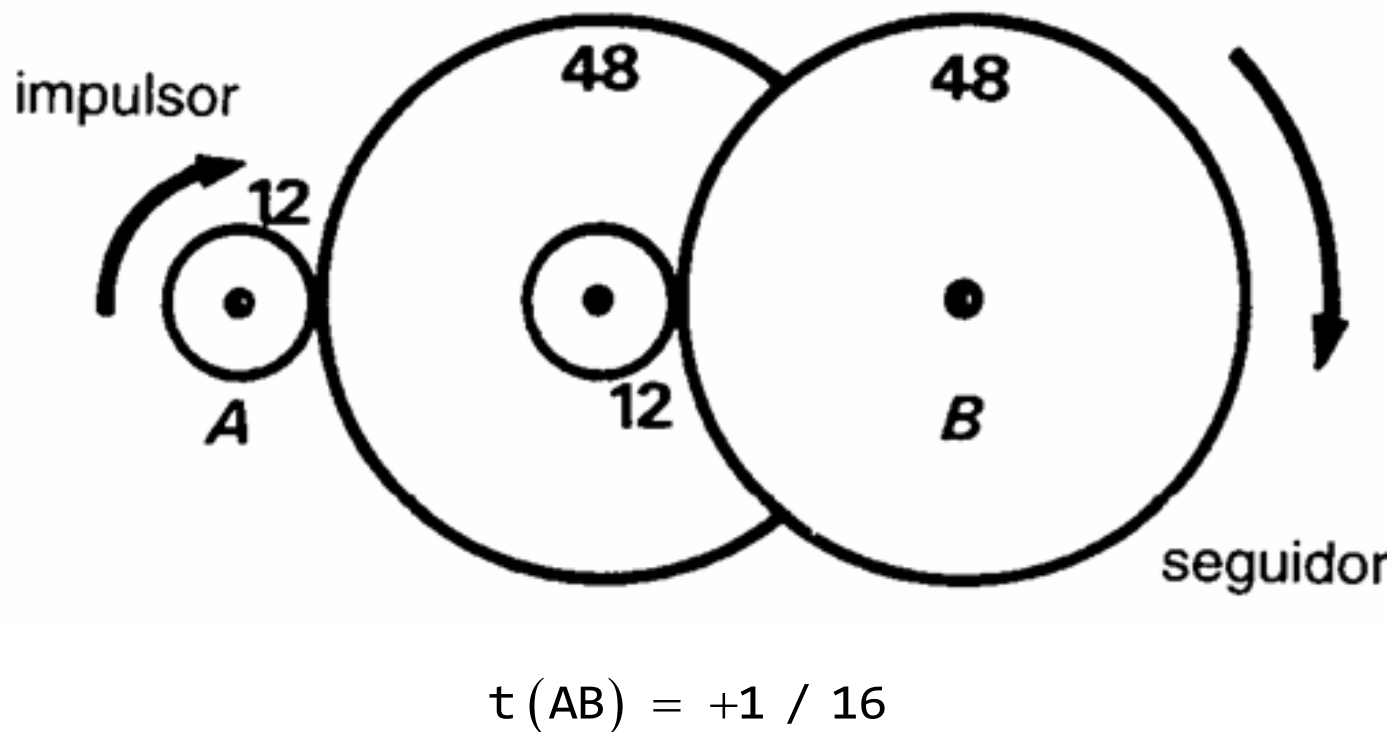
Tren de Engranajes Compuesto en un Cabrestante.
